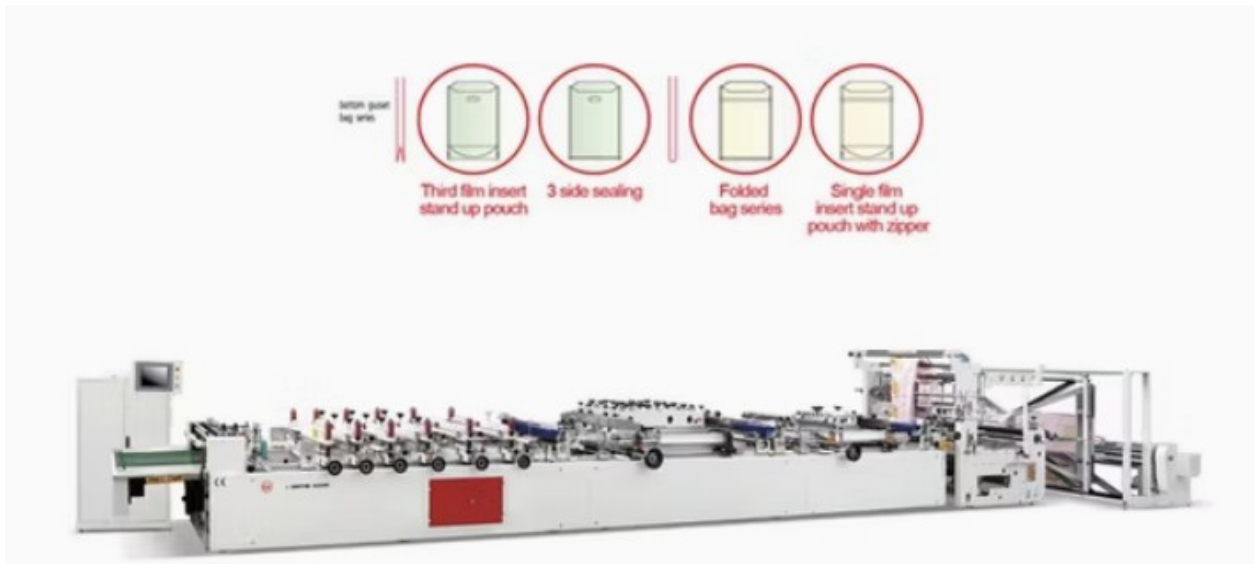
Машина для виготовлення дой-паків CWZD-600C+FD
